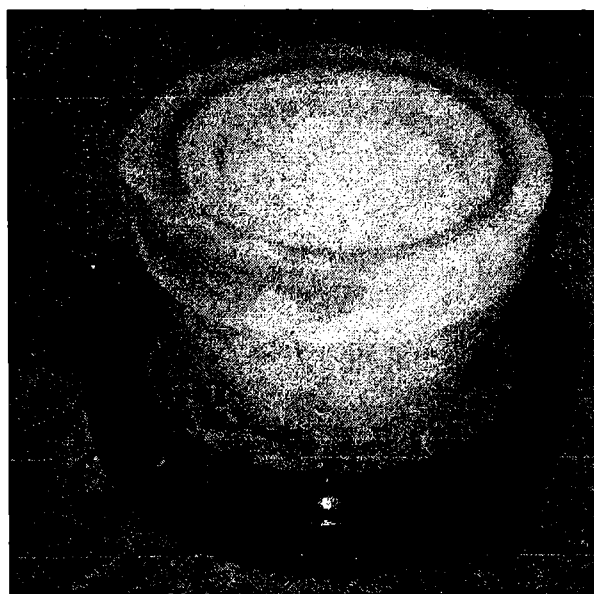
Общий вид отливки «Переход», извлеченной из формы.
